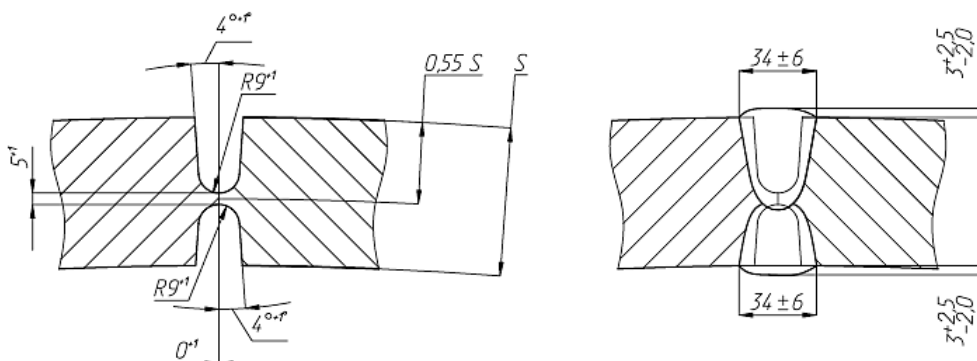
а) разделка кромок под сварку с углом $4^{\circ+1^{\circ}}$, б) выполненное сварное соединение
